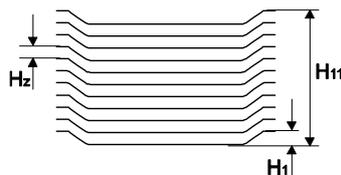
Altezza della pila intermedia H_z per 11 pezzi di stoviglie
